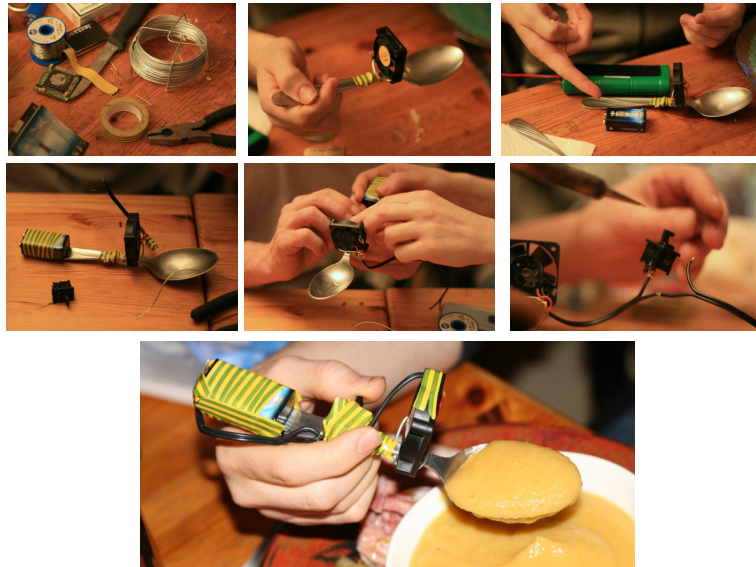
Étapes de construction d'un refroidisseur à soupe
